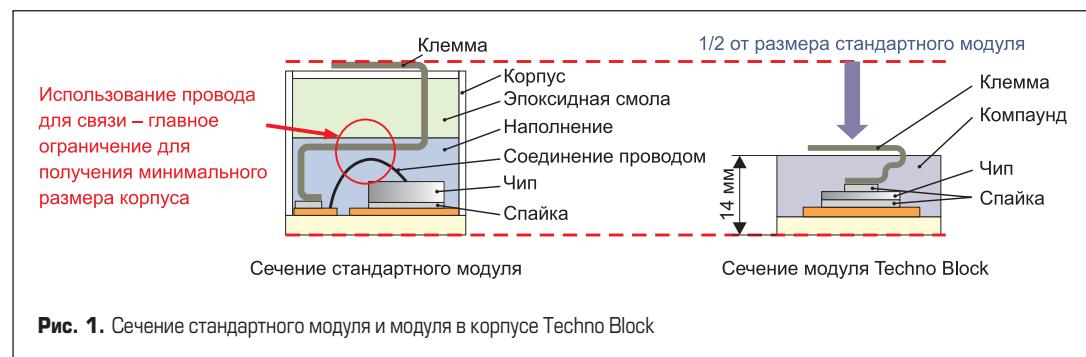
Сечение стандартного модуля и модуля в корпусе Techno Block
